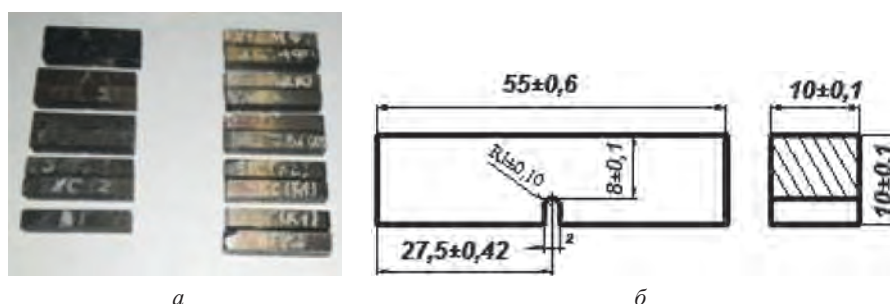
Опытные стальные образцы для определения их ударной вязкости: *а* – вид образцов, изготовленных из различных сталей; *б* – чертеж образца
